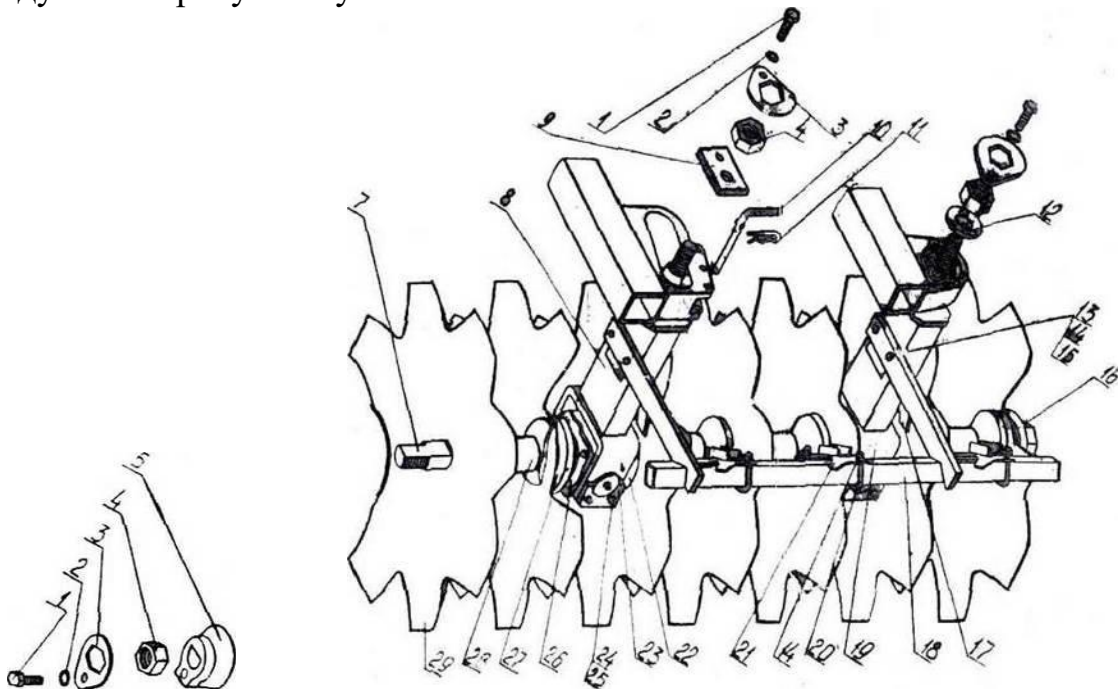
Дискова батарея: 1 - болт; 2 - шайба; 3 - замок; 4 - гайка; 5 - шайба внутрішня; 7 - вісь батареї; 8 - стійка батареї, регульована; 9 - шайба спеціальна; 10 - штир; 11 - шплінт пружин; 12 - шайба; 13 - болт; 14 - гайка; 15 - шайба; 16 - шайба зовнішня; 17 - чистик; 18 - кронштейн чистиків; 19 - стійка батареї; 20 - хомут; 21 - чистик правий; 22 - упор опуклий; 23 - планка; 24 - болт; 25 - шайба; 26 - підшипниковий вузол; 27 - упор увігнутий; 28 - котушка; 29 - диск [1].
